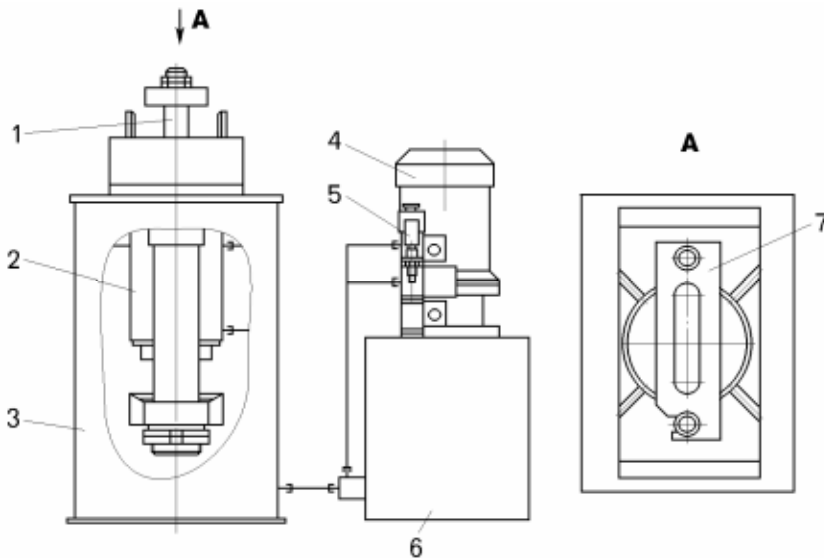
Установка для регулировки натяга манжеты:
